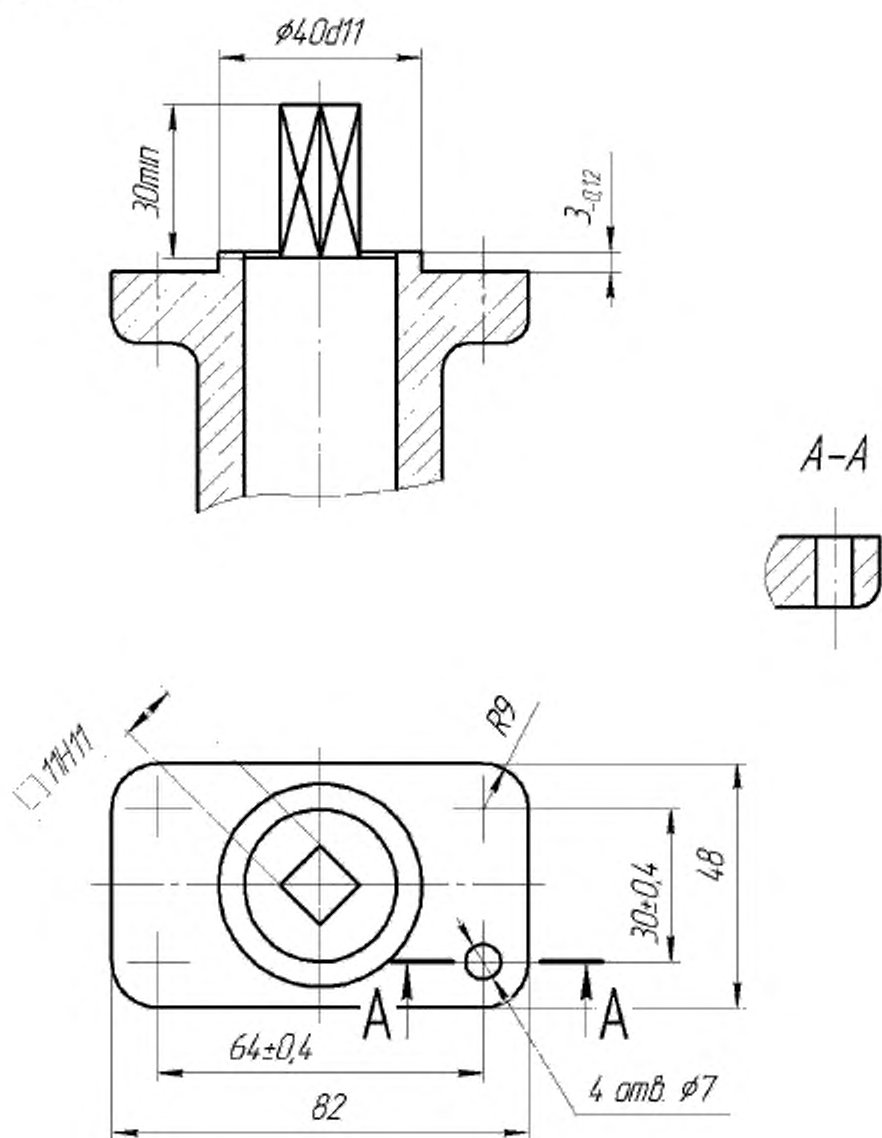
Ответное присоединение трубопроводной арматуры типа М4
